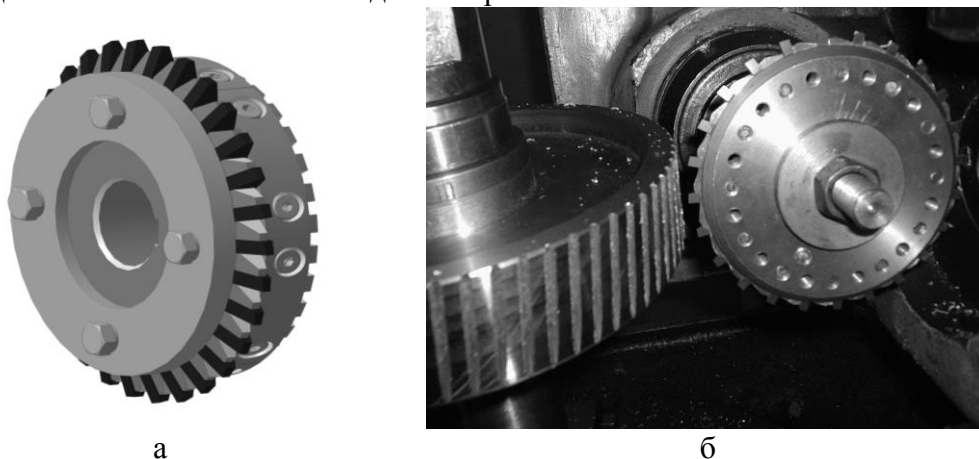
3D модель дискової збірної фрези з пластинами твердого сплаву (а) та нарізання синусоїдального колеса на зубофрезерному верстаті
